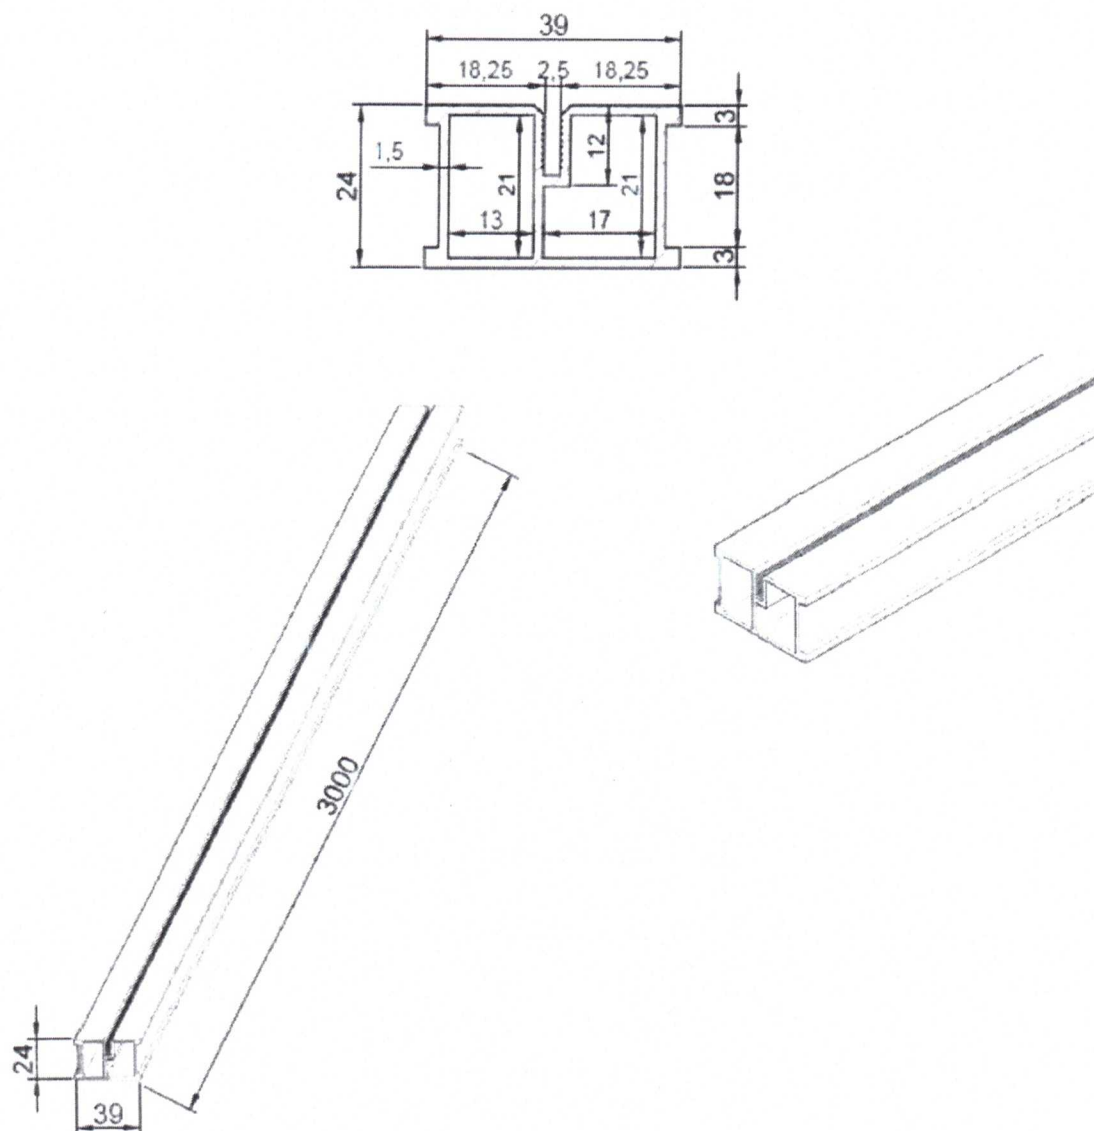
Viga de aluminio con sección transversal de 39 x 24 mm
